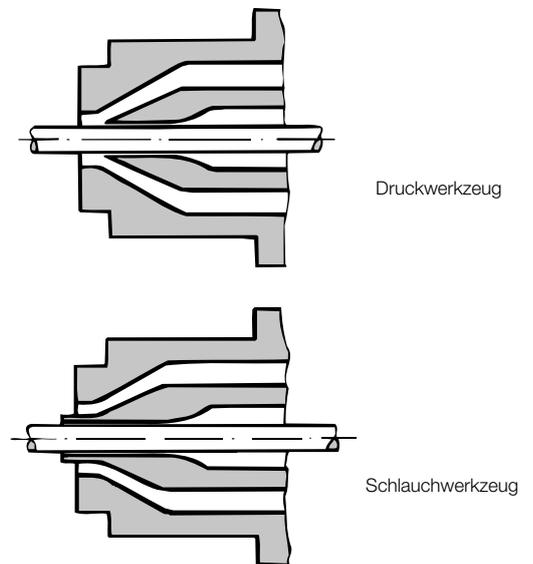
Draht- und Kabelummantelungswerkzeuge
